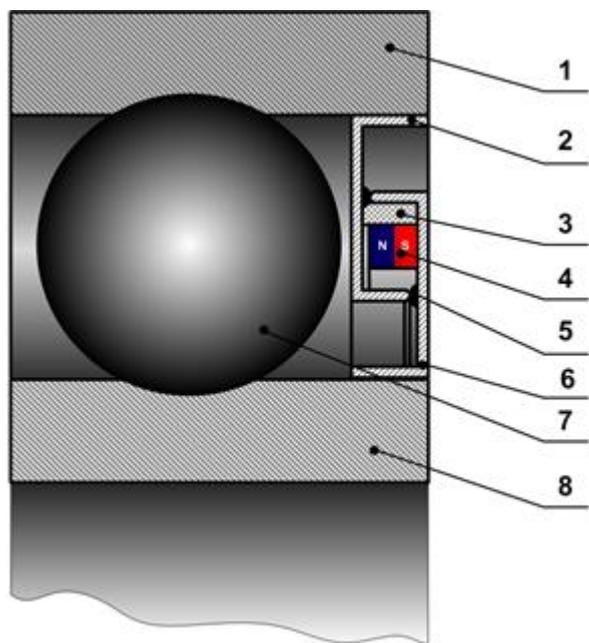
Подшипник качения с магнитожидкостным уплотнением:
